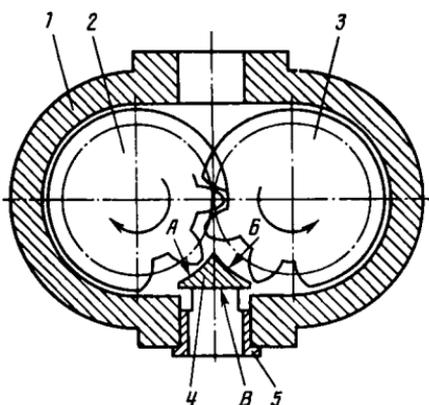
Схема шестеренного гидромотора с устройством для улучшения пуска:
